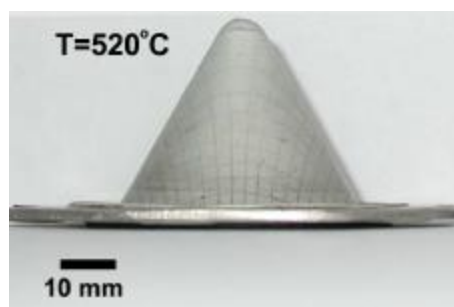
Образец сплава 1570С, полученный сверхпластической формовкой из листовой заготовки.
